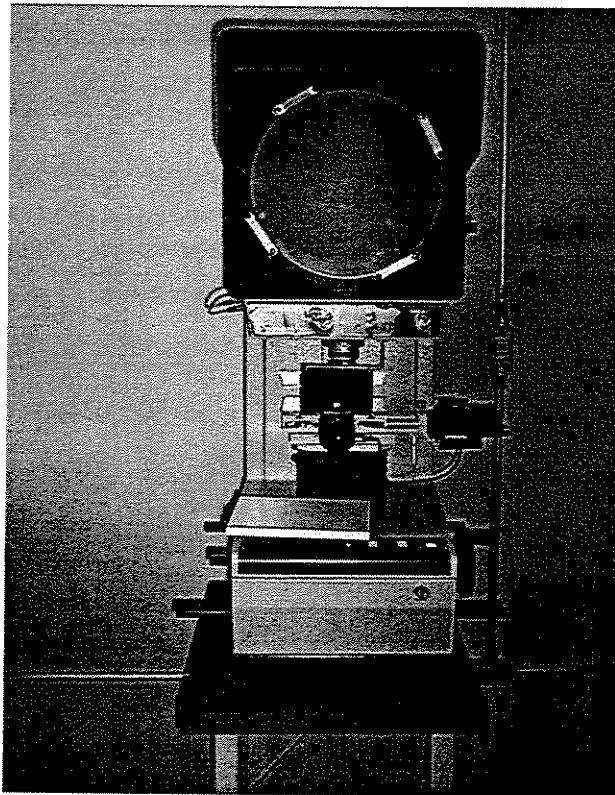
Projetor de perfil utilizado nos ensaios
